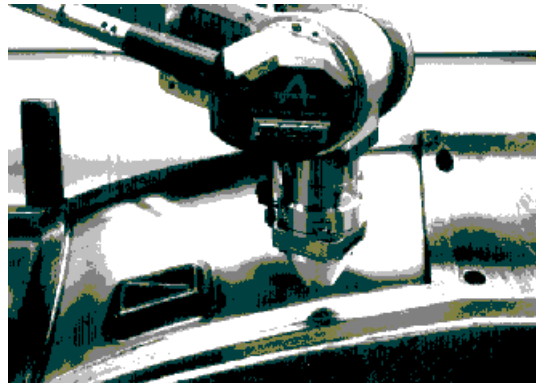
Bearbeitungskopf im Einsatz beim Härten eines Spritzgußwerkzeuges (TLT)
